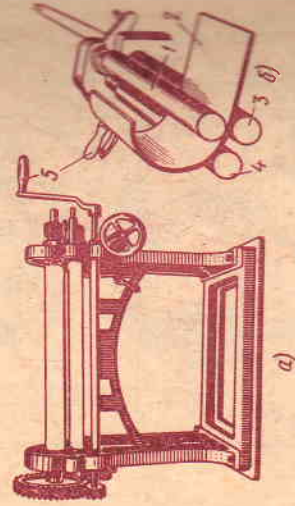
Правка листового и полосового металла с помощью ручных гибочных вальцовок:
